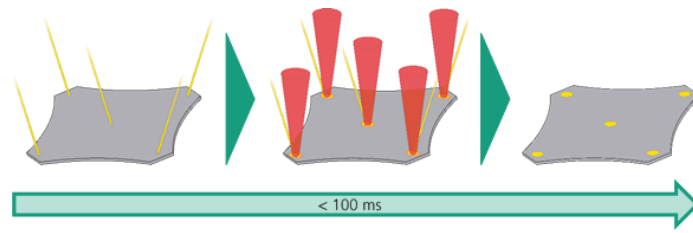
Prozessablauf beim Mikro-Laserauftragschweißen
